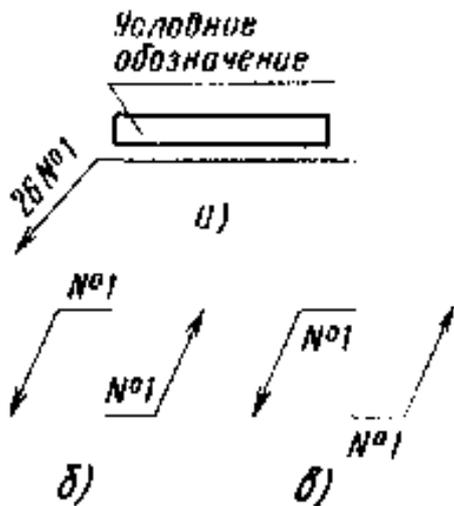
Условное обозначение одинаковых сварных швов
